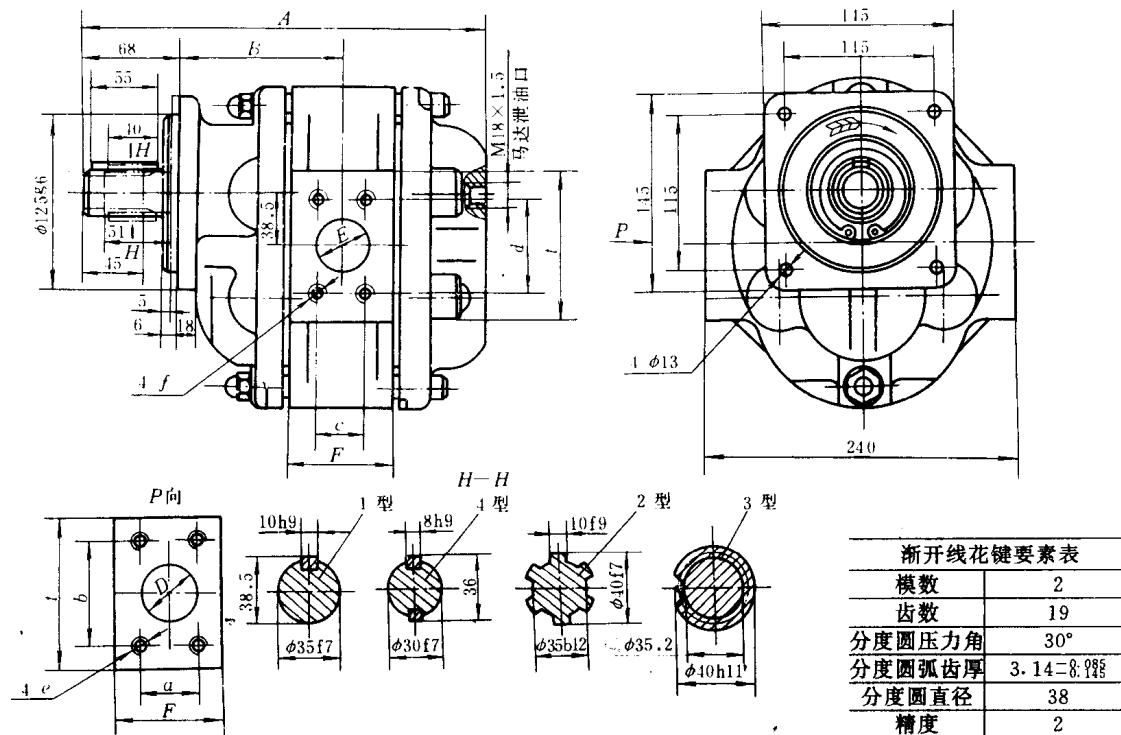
CBG3 (CMG3) 齿轮泵 (齿轮马达)
